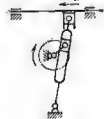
Многозвенный плоский кривошипно-кулисный механизм привода поперечно-строгольного станка.
